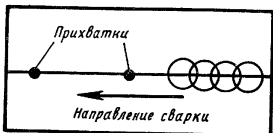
Схема сварки методом последовательного образования сварочных ванночек
